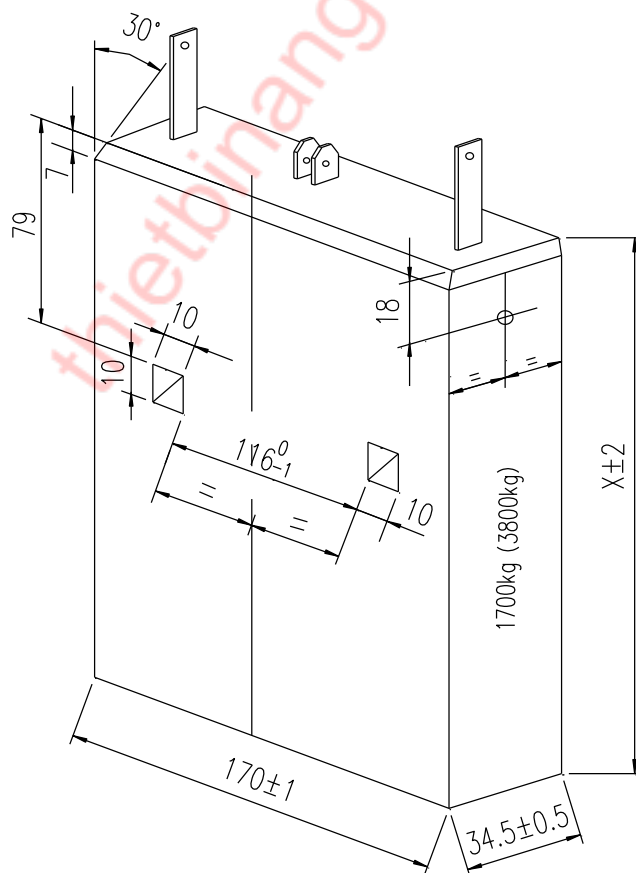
配重 Fig. 2-22 Counter-jib ballast
